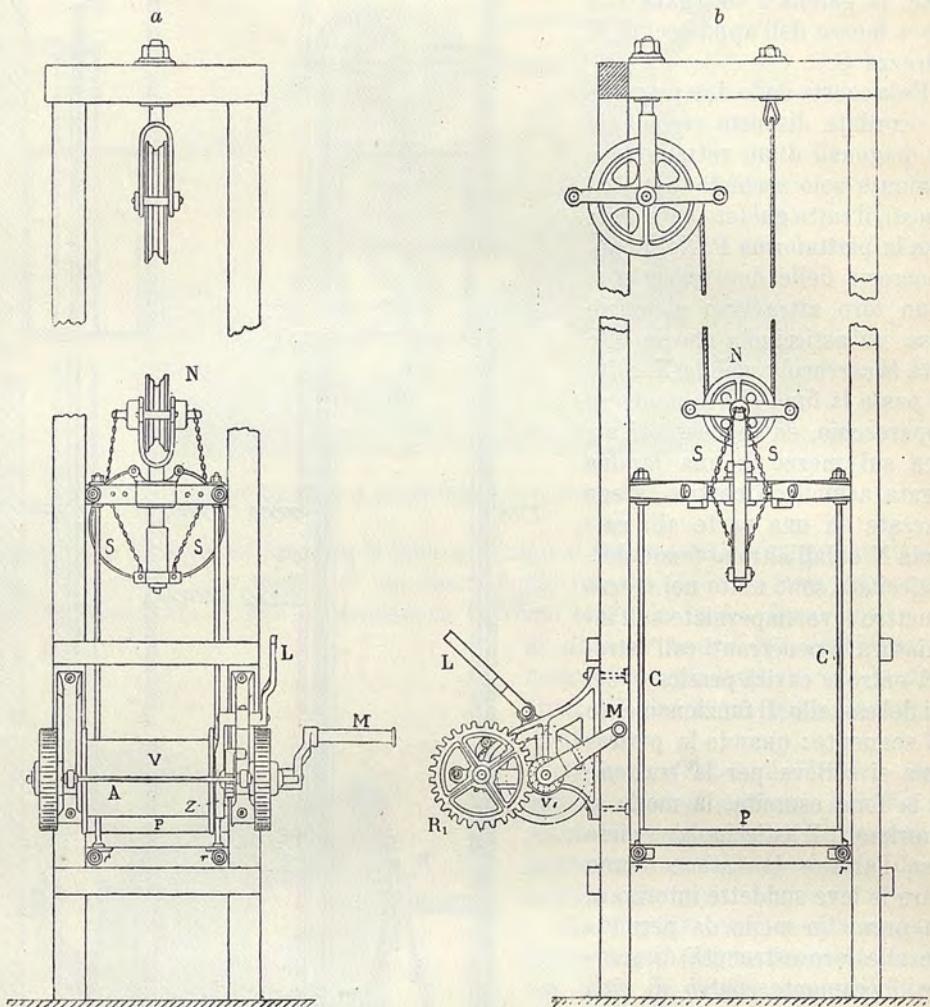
Elevatore per proiettili nel forte di Exilles.
